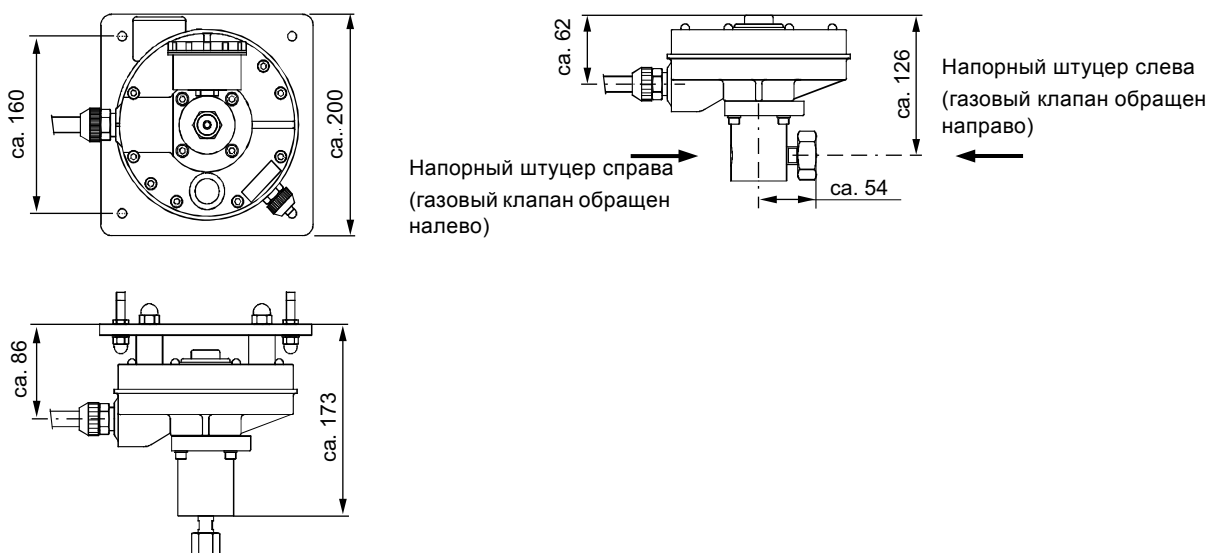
Масштабный чертеж вакуумного регулятора на монтажной пластине
